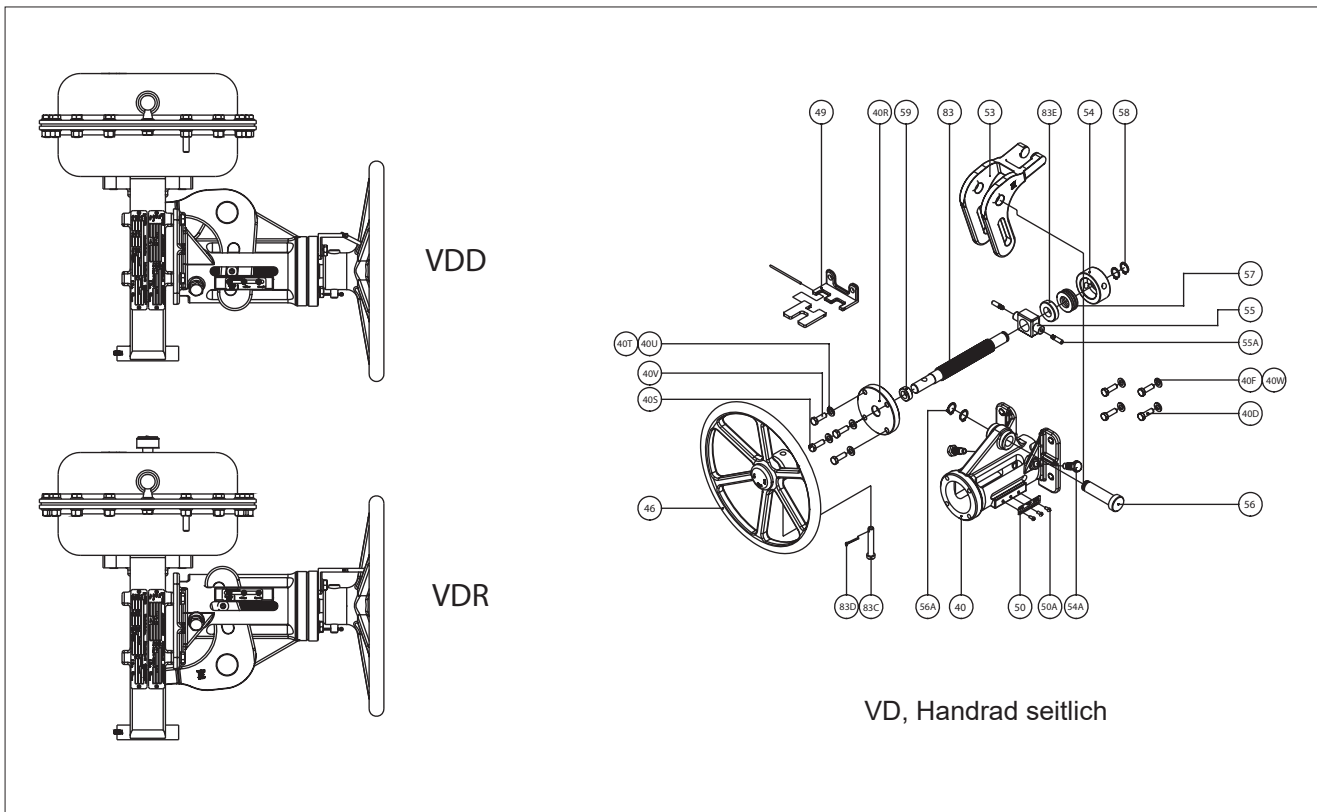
VD\_25/29/37, Antriebs-Konstruktion mit Handrad
